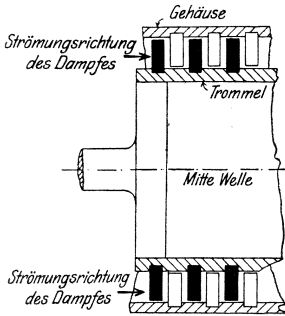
Teilweiser Schnitt durch eine Dampfturbine.
